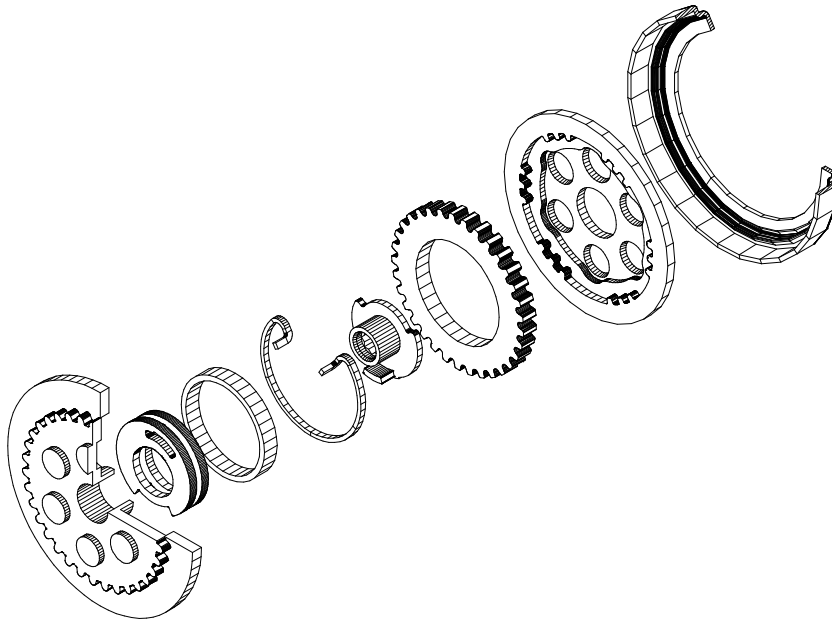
Explosionszeichnung Taumelbeschlag [26]
